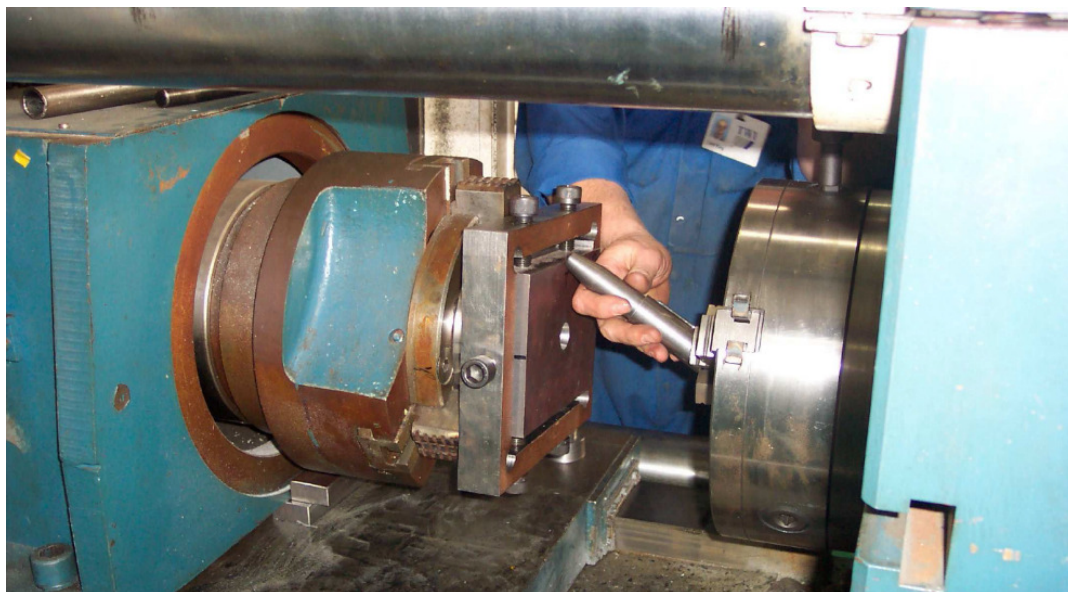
Máquina de soldagem por atrito NEI (LESSA, 2011).
